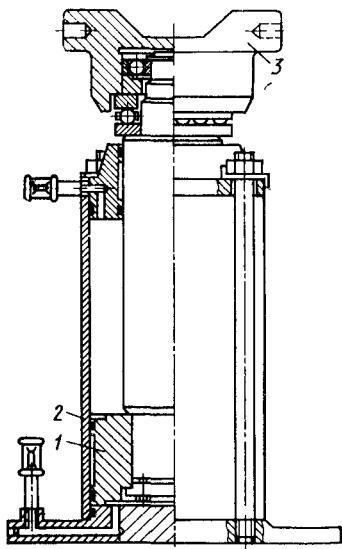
Подъемно-поворотный стол для разворота слитков и поковок
